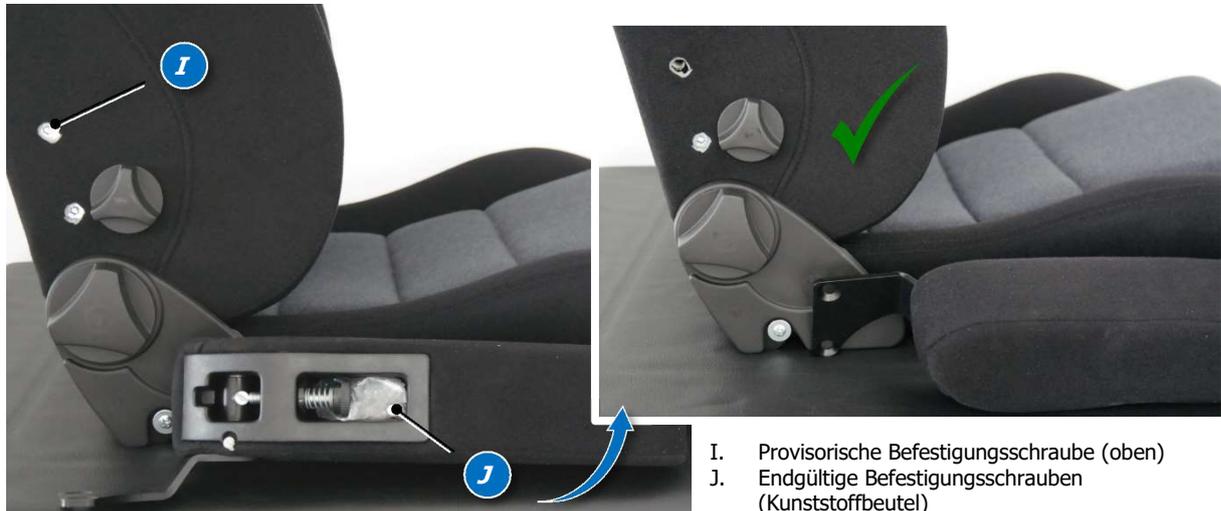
Montage der Armlehnen (Option) - Provisorische Befestigungsschraube (oben) entfernen
